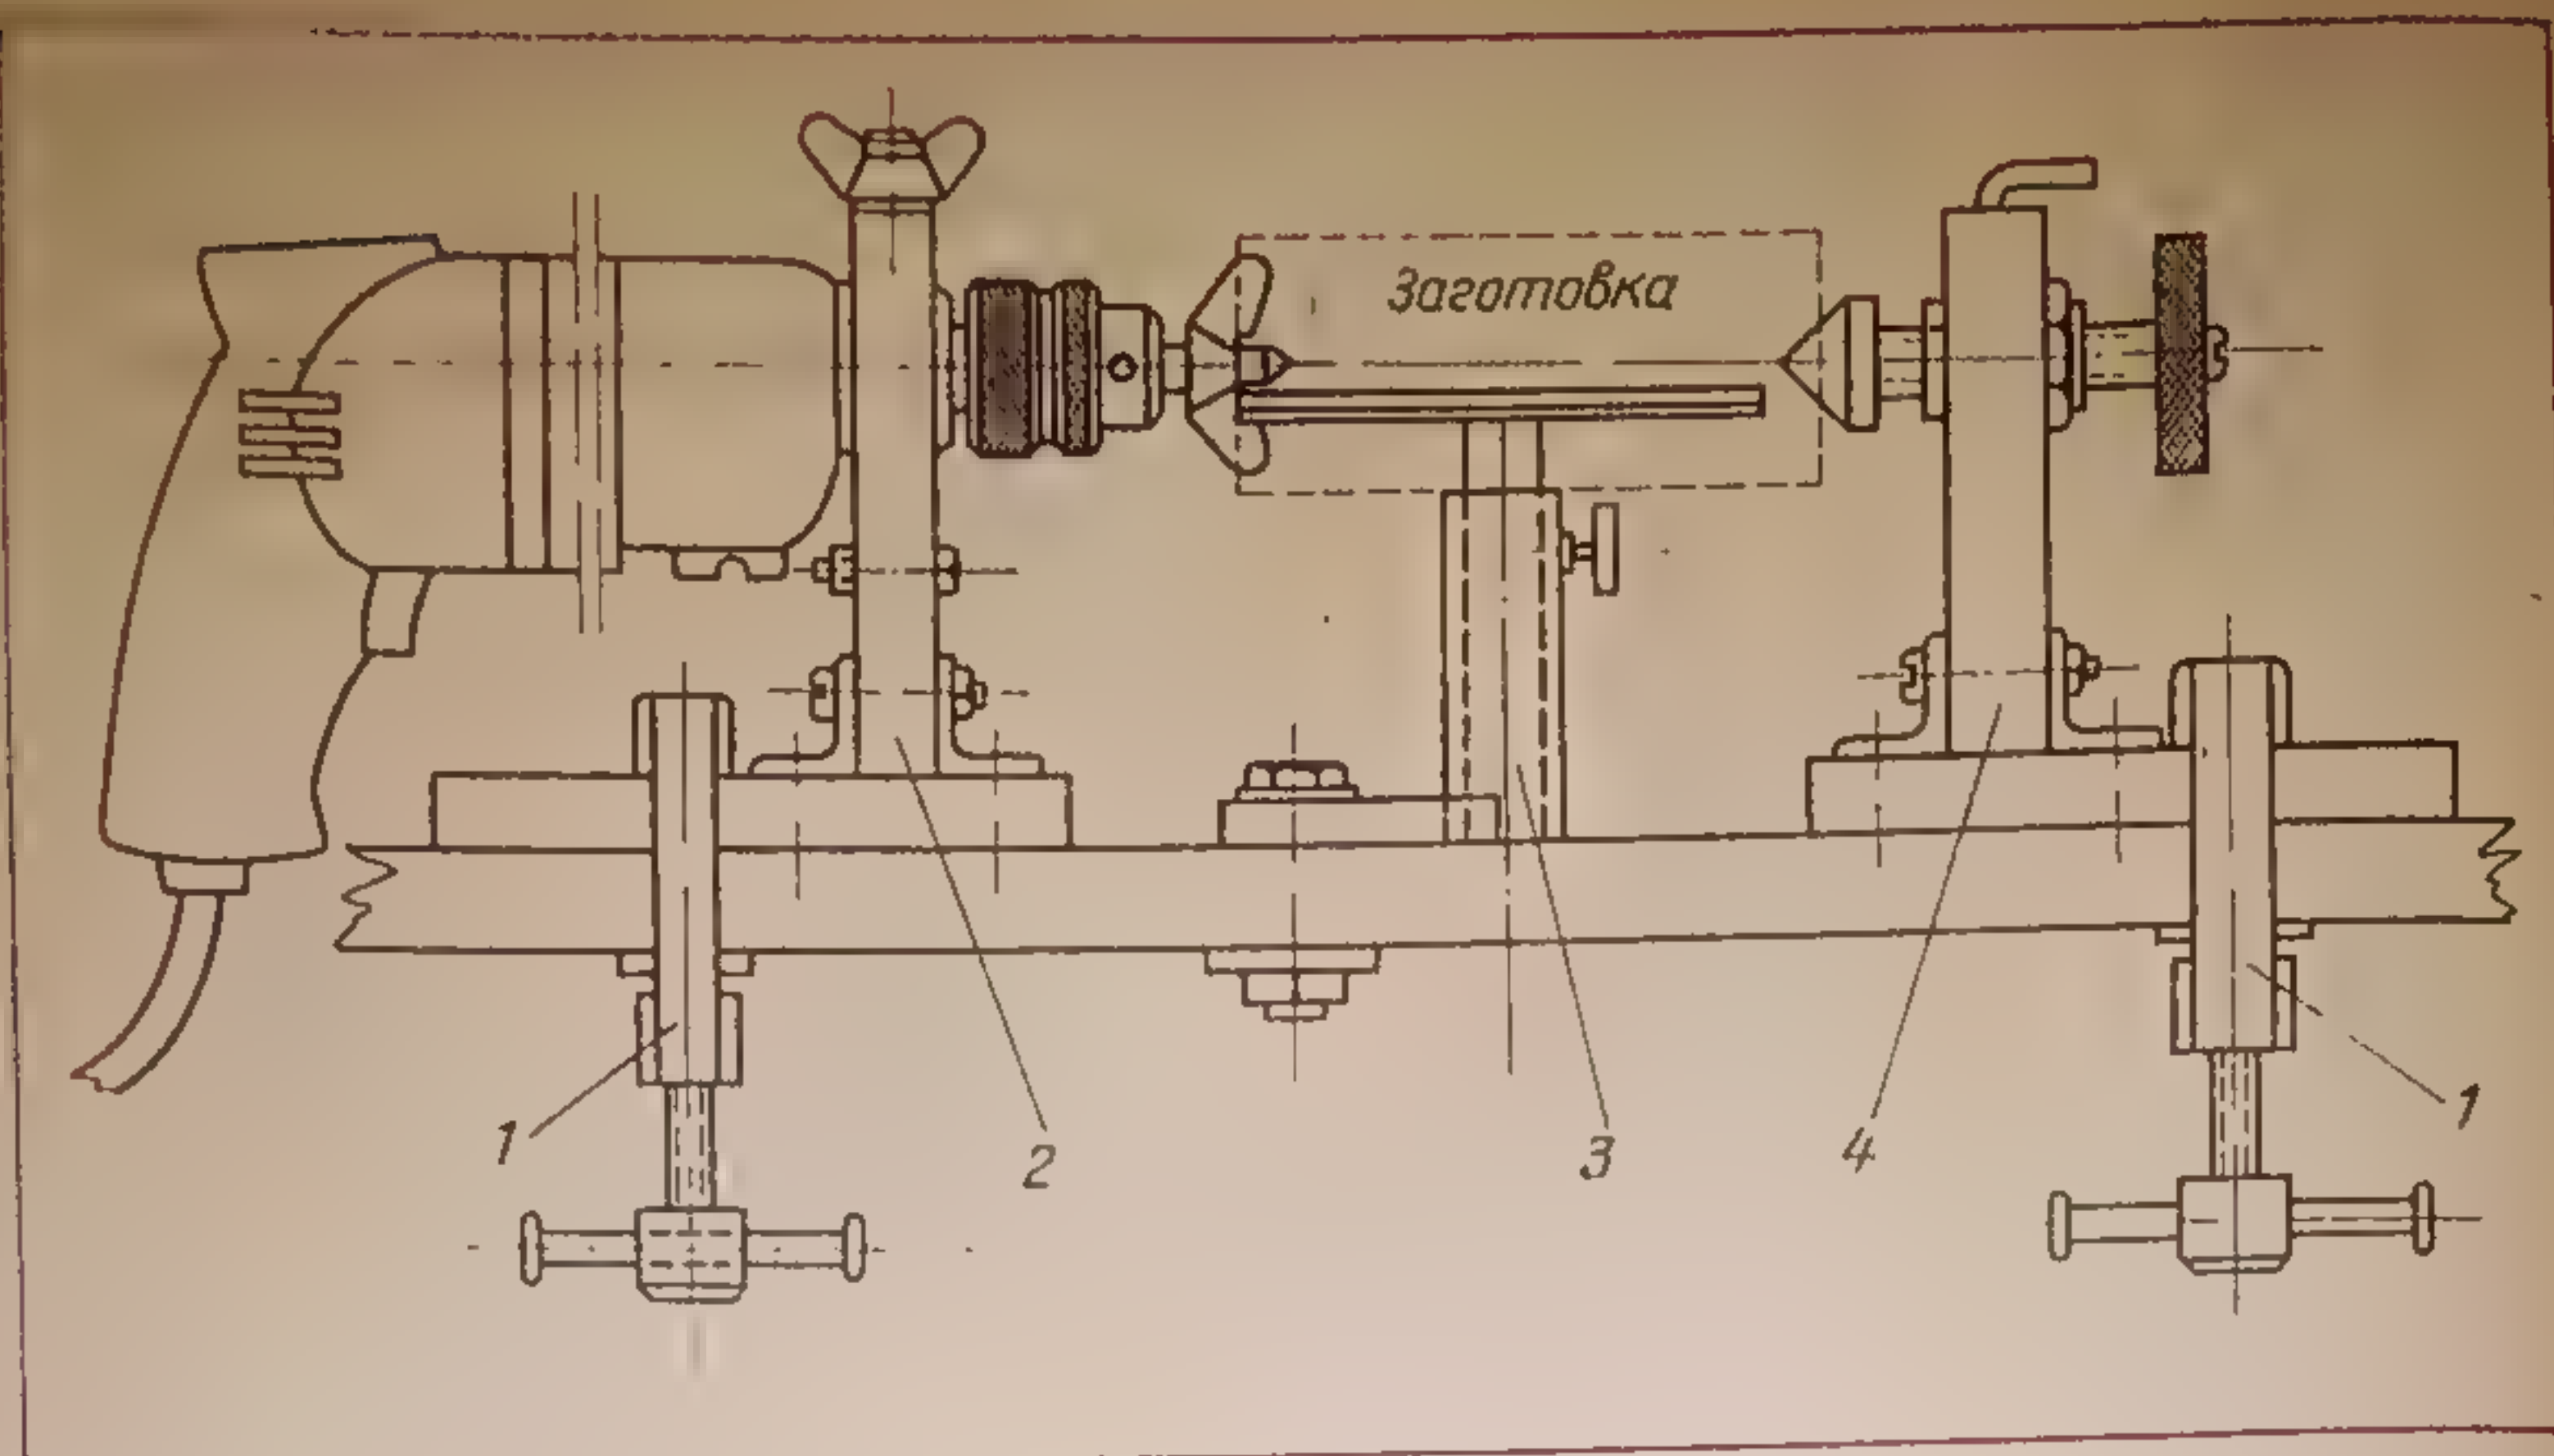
Токарный станок на основе электродрели: 1 — струбцина; 2 — передняя бабка; 3 — упор для резца; 4 — задняя бабка
